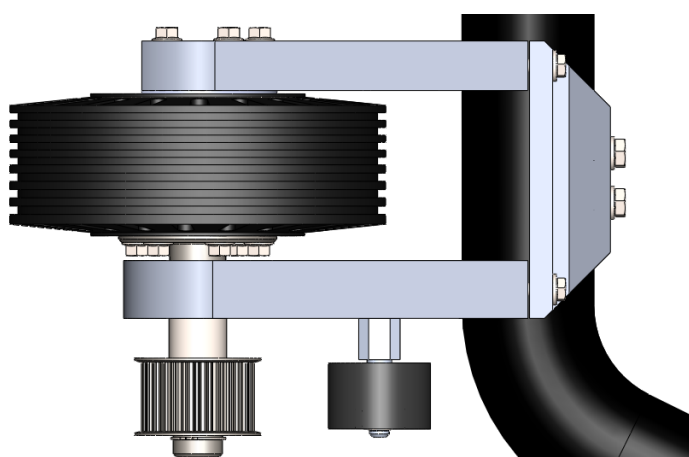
| Montagem da solução adotada para o motor de tração, suporte frontal.
